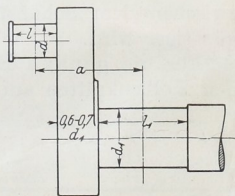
Skizze der Stirnkurbel zur Maschine
